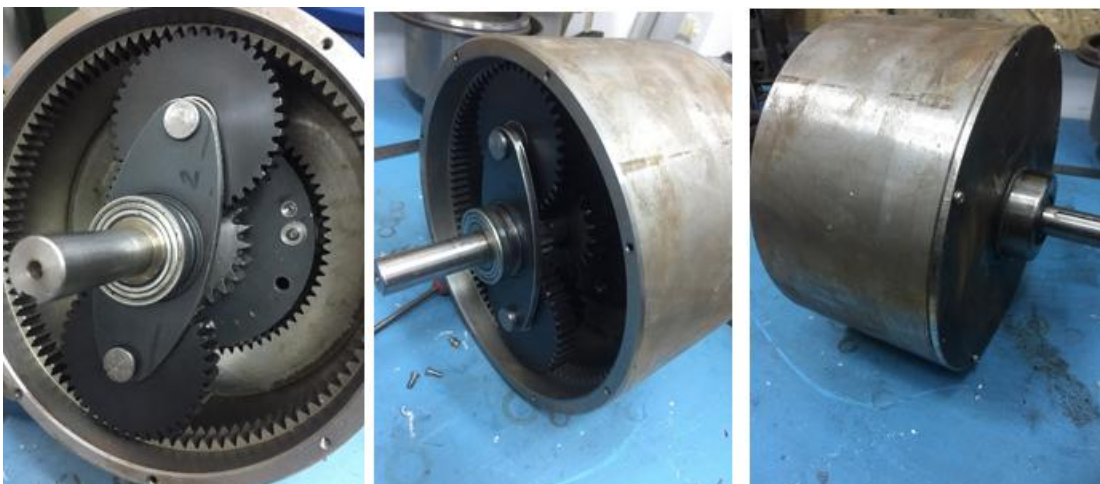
Опытный образец адаптивного привода схвата робота
